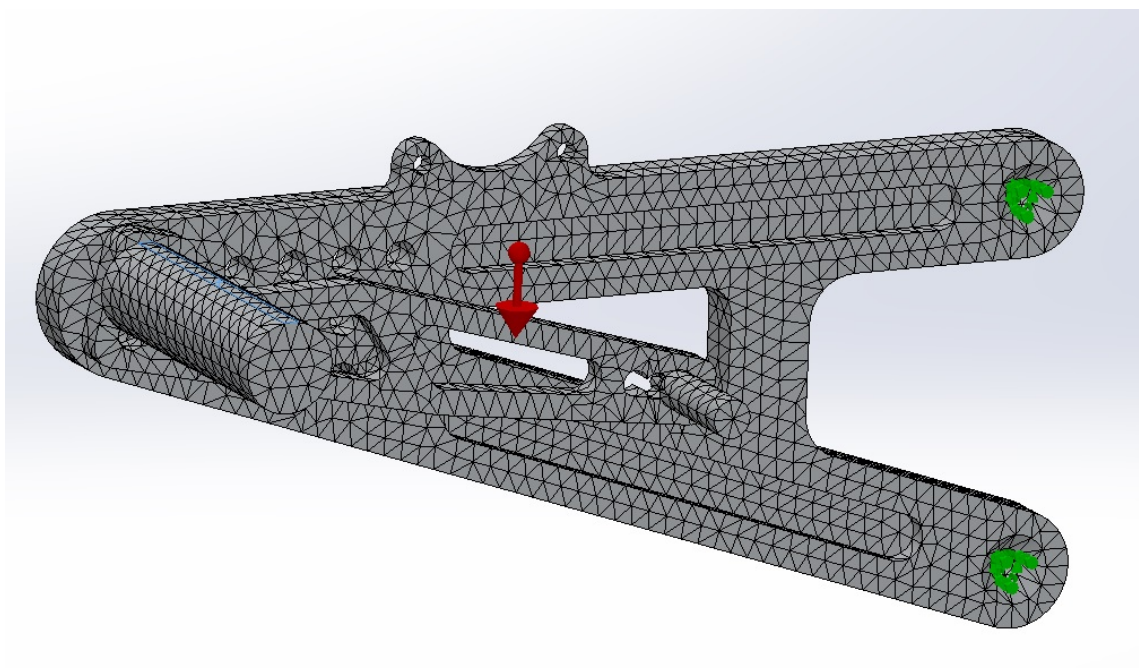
Mallado y cargas aplicadas (Primer diseño estribera derecha).
